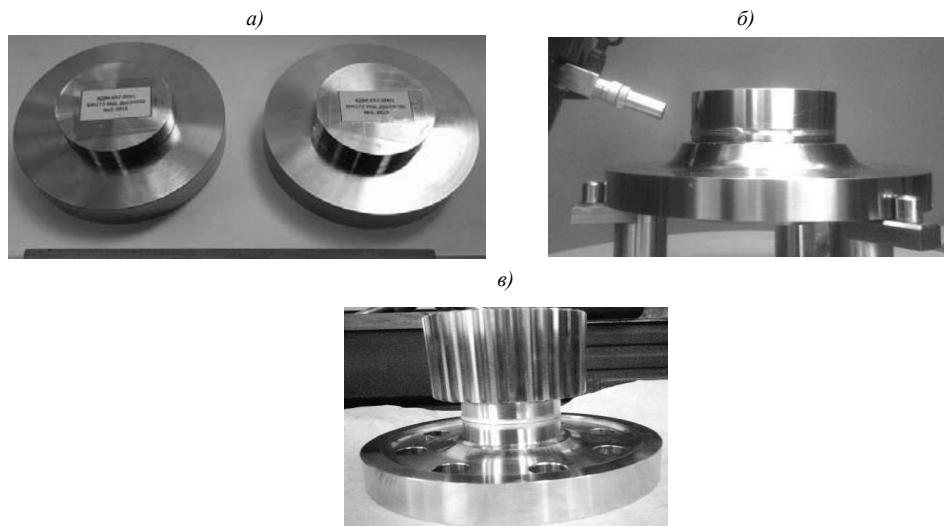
Заготовки для ротора ГТД из сплава ВЖ172-ИШ:
